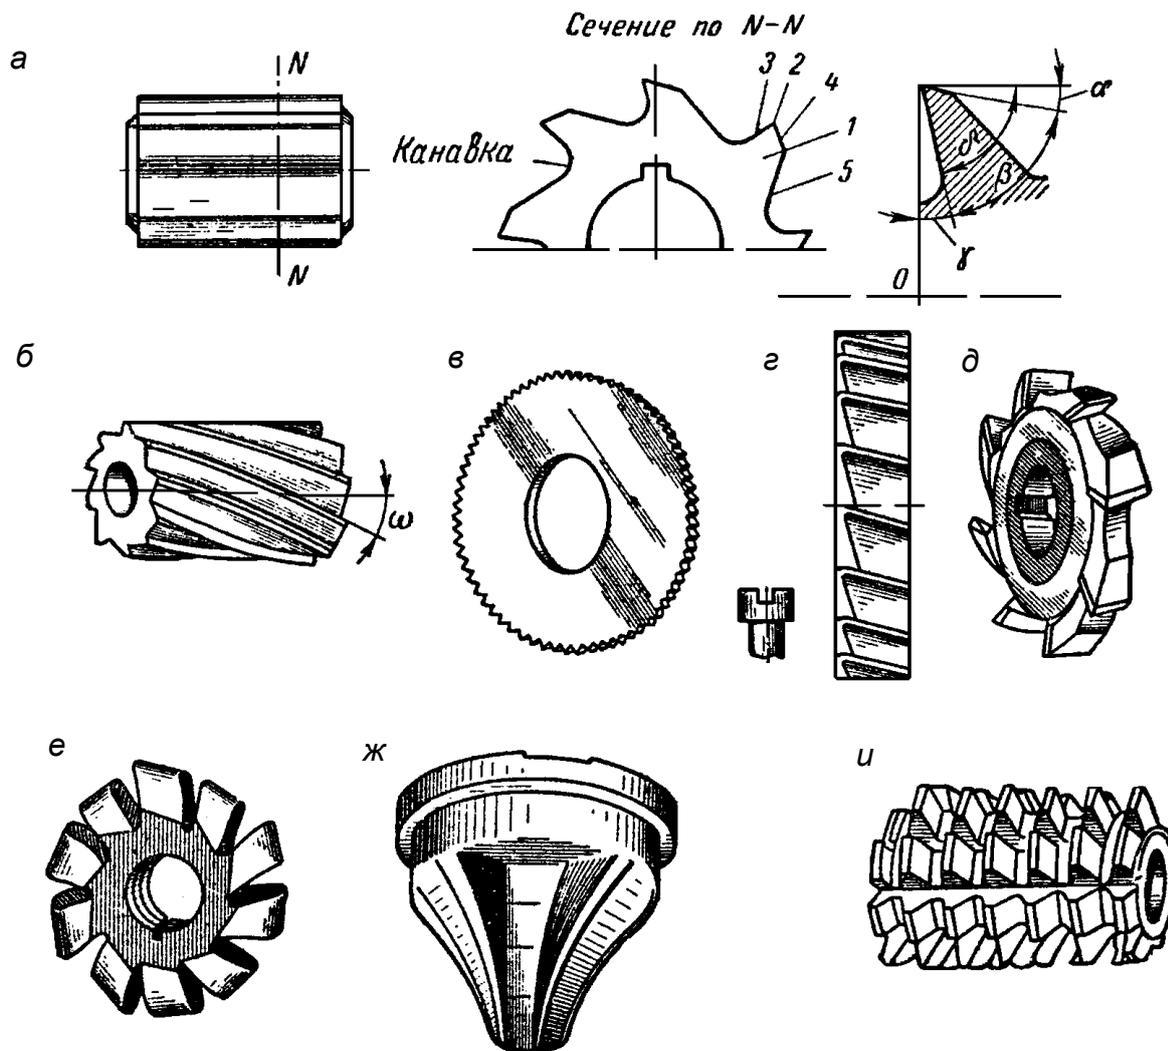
Основные типы фрез: а – цилиндрическая прямозубая; б – цилиндрическая с винтовыми зубьями; в – дисковая пазовая; г – дисковая двухсторонняя; д – дисковая трехсторонняя; е – модульная дисковая; ж – мо-
